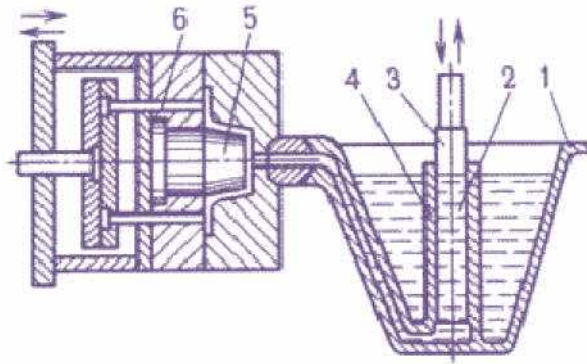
Схема виготовлення відливки на машинах з гарячою камерою пресування
